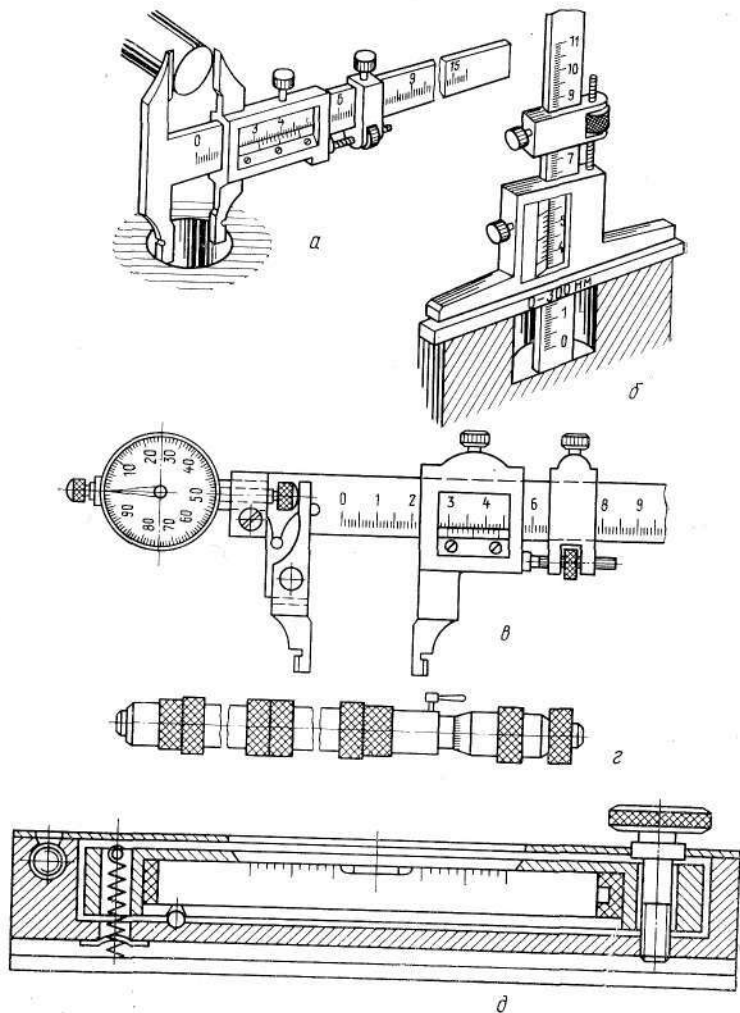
Инструменты для контроля точности сборки и установки машин:
